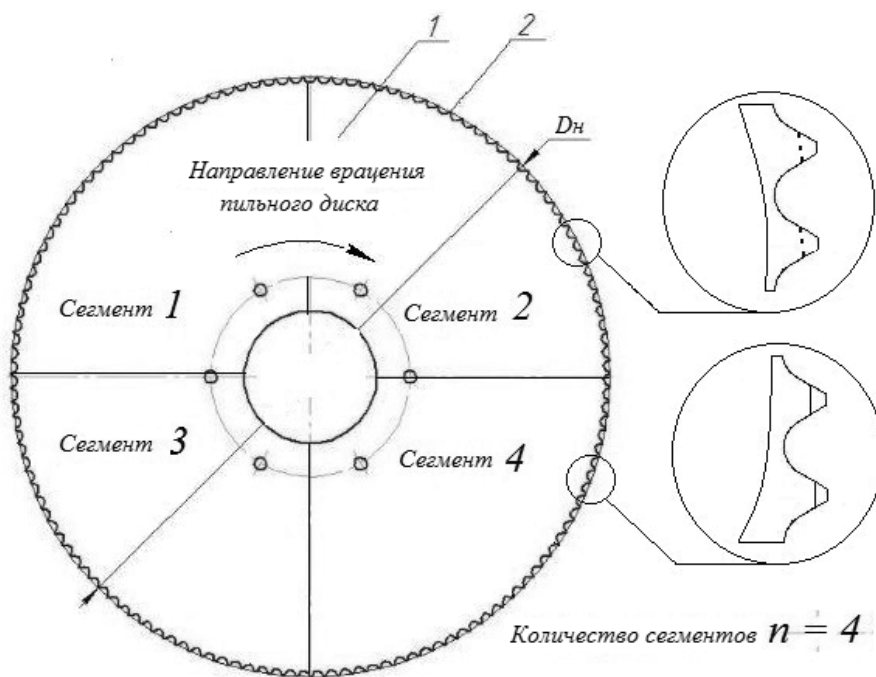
Дисковая пила стана «800» для порезки крупногабаритных фасонных и сортовых прокатных профилей с сегментарной компоновкой групп режущих зубьев, общий вид: 1 – корпус; 2 – призматические режущие зубья
